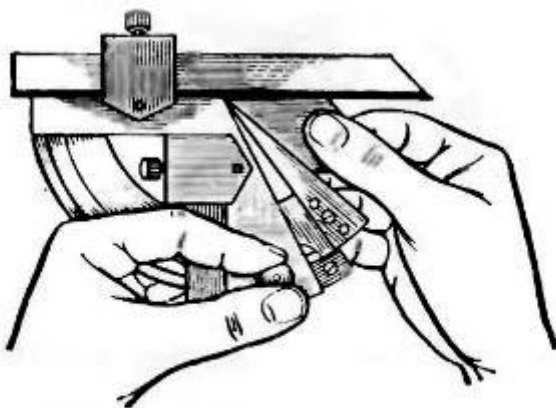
Установка угломера относительно наружного угла незакрепленной детали при помощи микроподачи
